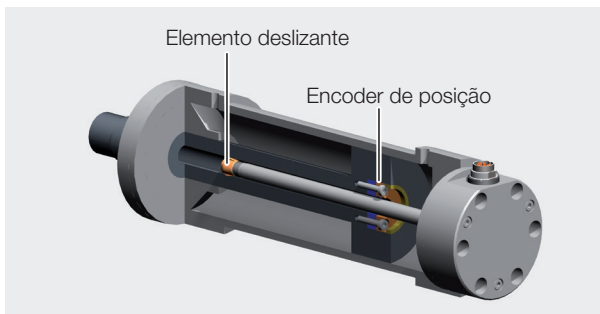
Exemplo 1, BTL instalado com elemento deslizante
